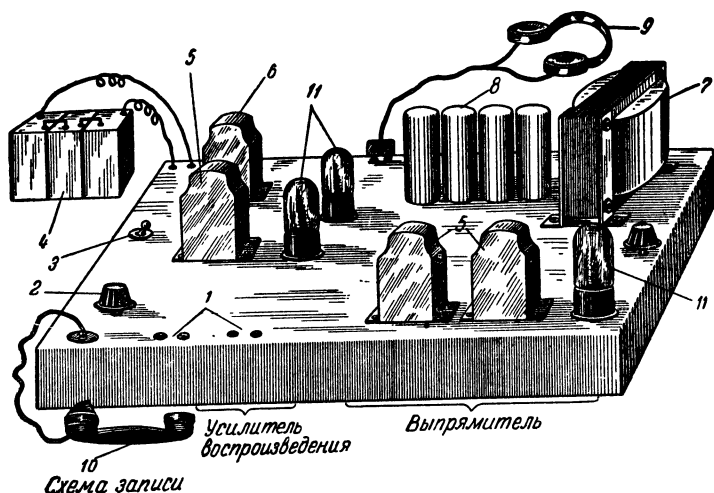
Примерное расположение деталей электрической схемы: 1 — гнезда для включения магнитной головки; 2 — регулятор тока подмагничивания; 3 — выключатель батареи; 4 — батарея; 5 — дроссели; 6 — трансформатор низкой частоты; 7 — силовой трансформатор; 8 — электролитические конденсаторы; 9 — головные телефоны; 10 — микрофон; 11 — радиолампы
